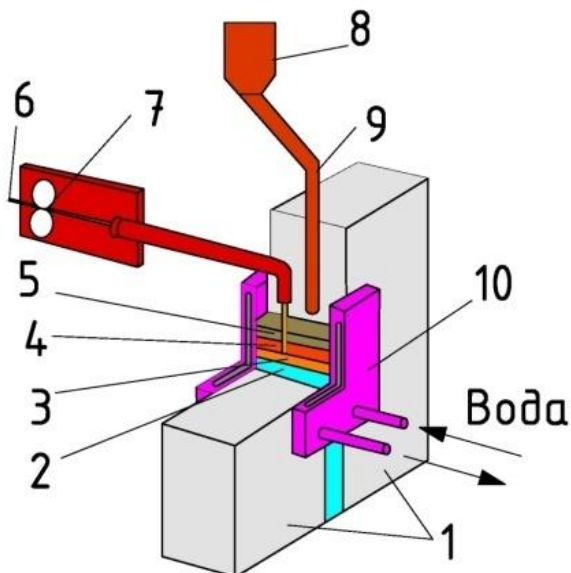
Принципиальная схема АСТ: 1 - Свариваемые детали; 2 – металл сварного шва; 3 - сварочная ванна; 4 – жидкий шлак; 5 – слой флюса; 6 – сварочная проволока; 7 – механизм подачи проволоки; 8 – дозатор флюса; 9 – подвод флюса в зону сварки; 10- медный водоохлаждаемый ползун
